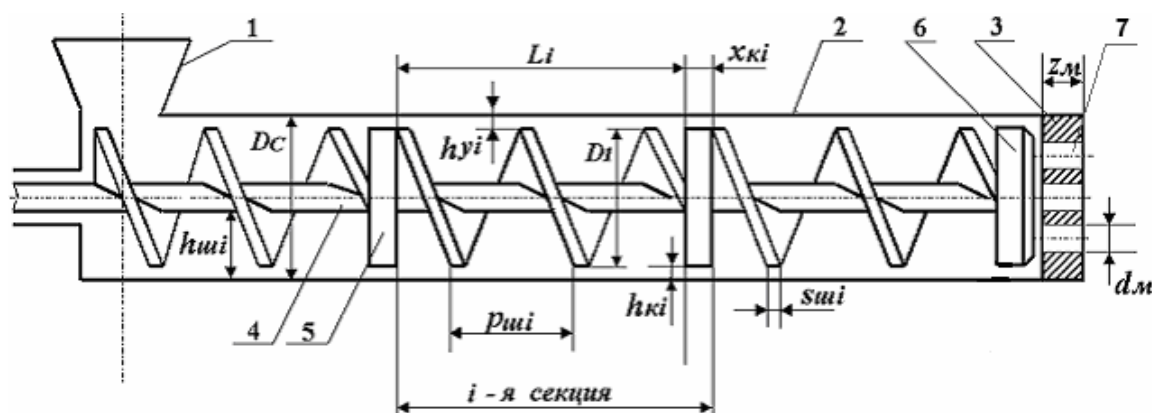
Схема прессующего механизма: 1– загрузочное устройство; 2– шнековый цилиндр; 3– матрица; 4– шнек; 5– компрессионный затвор; 6– головка экструдера; 7– фильера.
